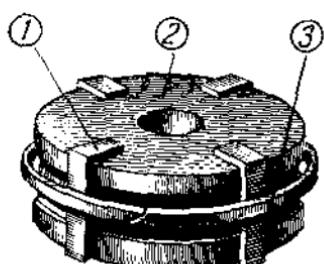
Приспособление для надевания поршневых колец на поршень.
